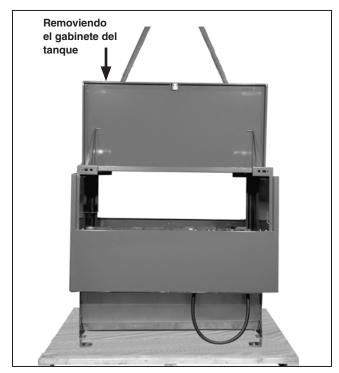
Un gabinete del interruptor Vista de montaje tipo pedestal siendo retirado del tanque.
